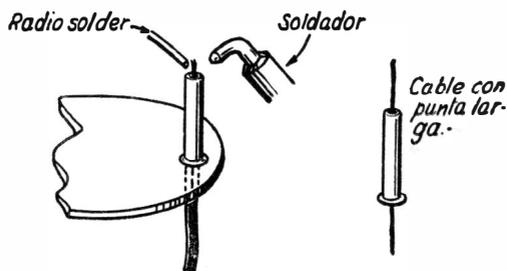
Forma de soldar el cable a la pata de una ficha.
